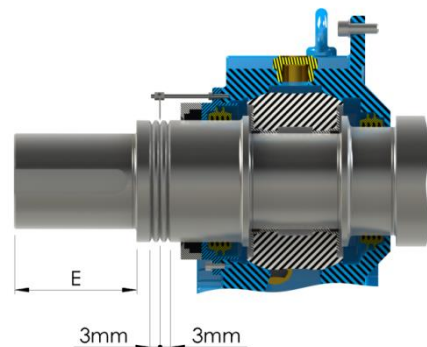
Выравнивание вала с подшипниками скольжения
